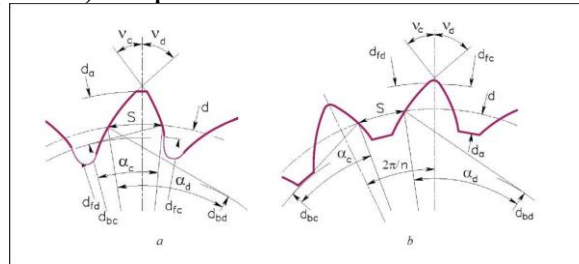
Профіль зубчастого профілю: а = зовнішня передача; b = внутрішня передача;  $d_a$  = діаметр кола наконечника зуба;  $d_b$  = діаметр базового кола;  $d_f$  = діаметр кола форми;  $v_c$  - шліфований робочий профіль асиметричного зубчастого колеса,  $v_d$  - неробочий профіль асиметричного зубчастого колеса
